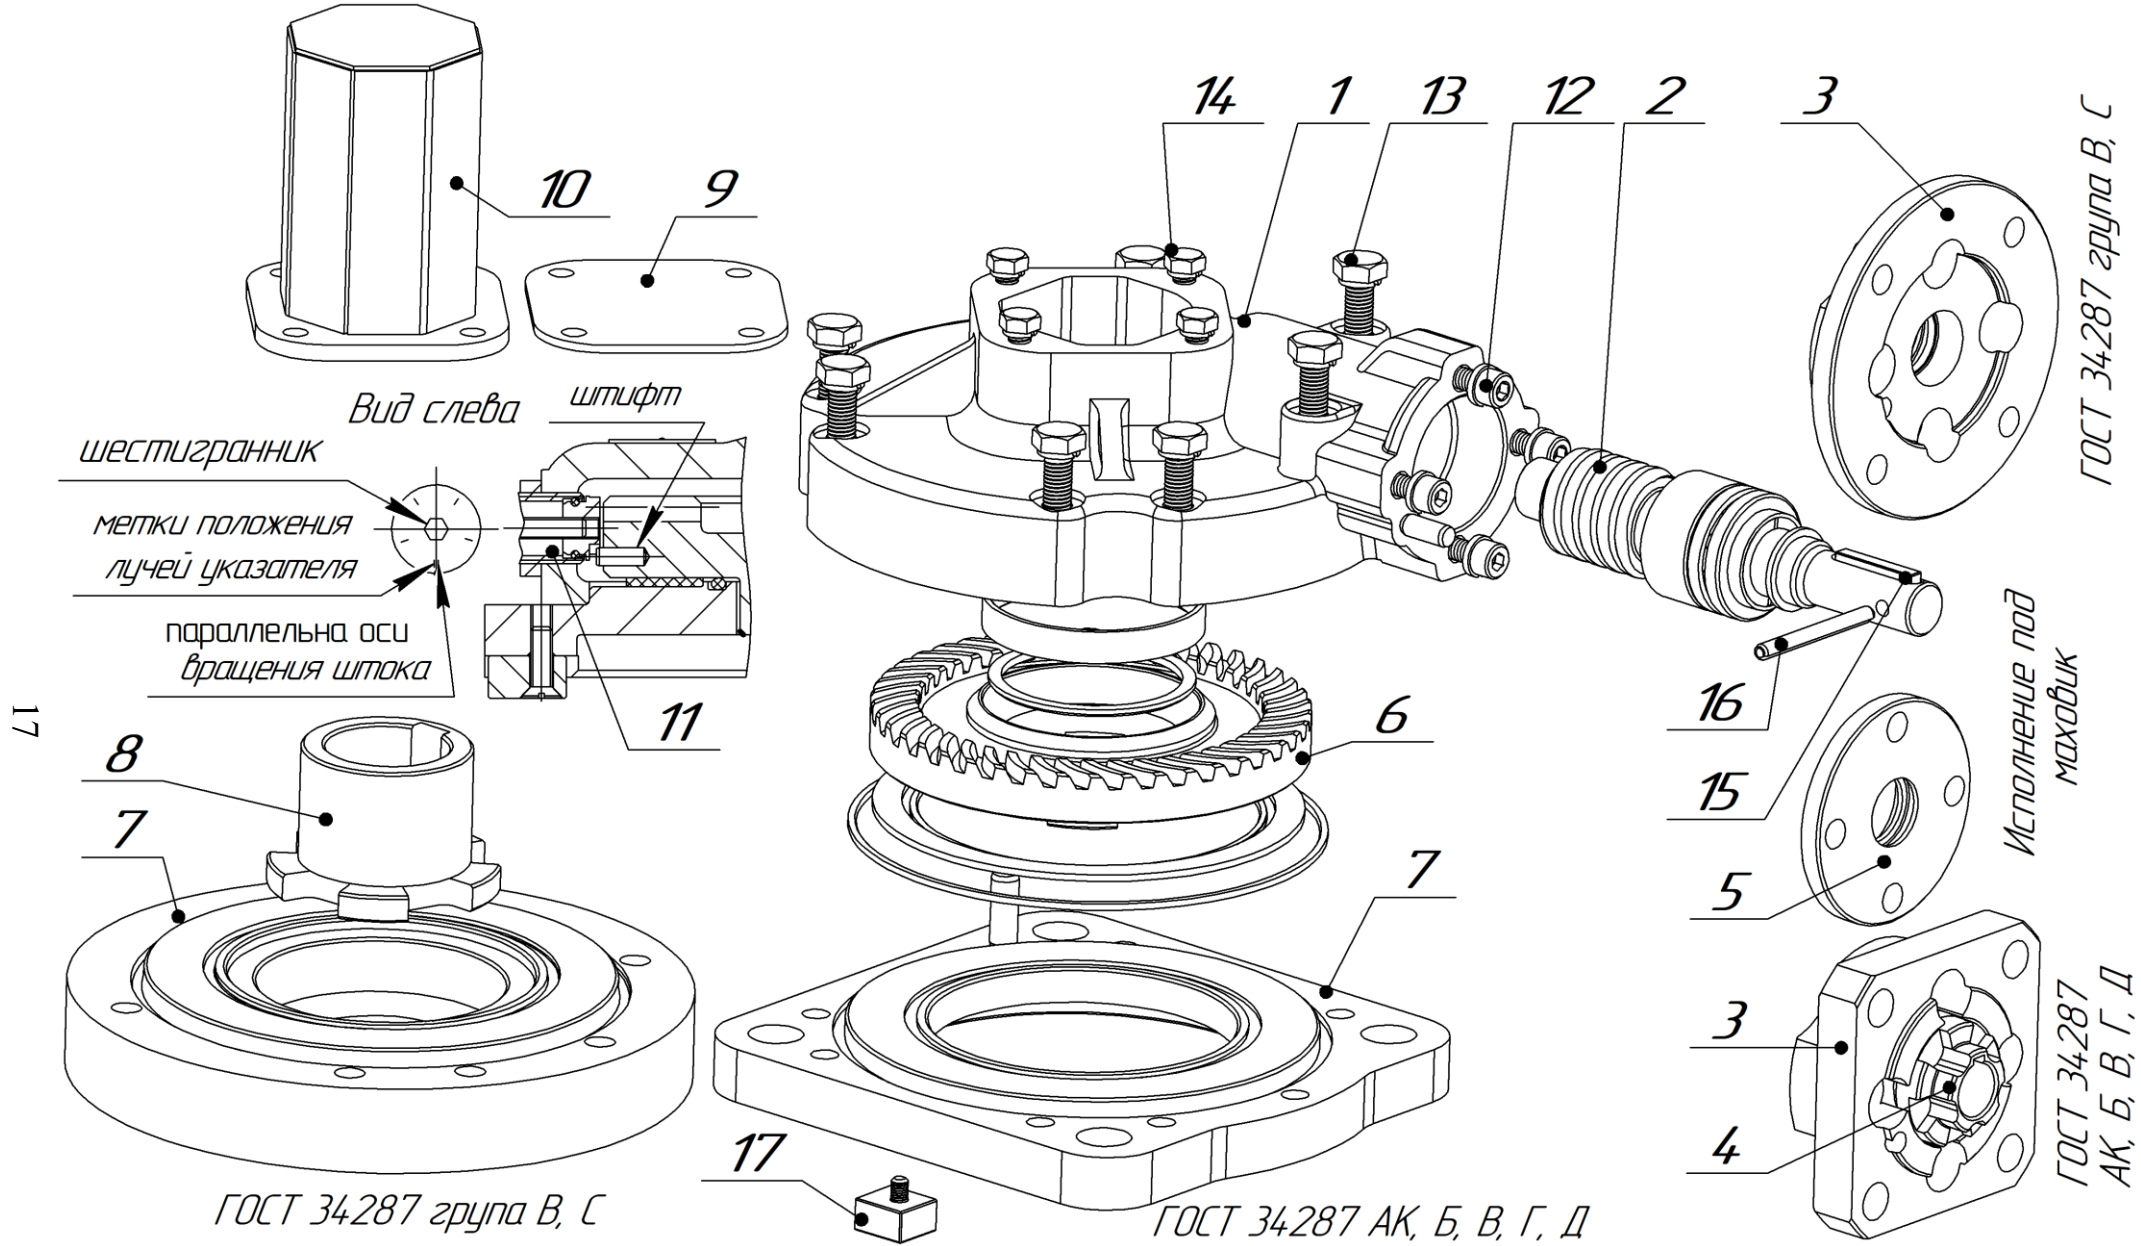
Одноступенчатый многооборотный редуктор модели РЗАМ-С
